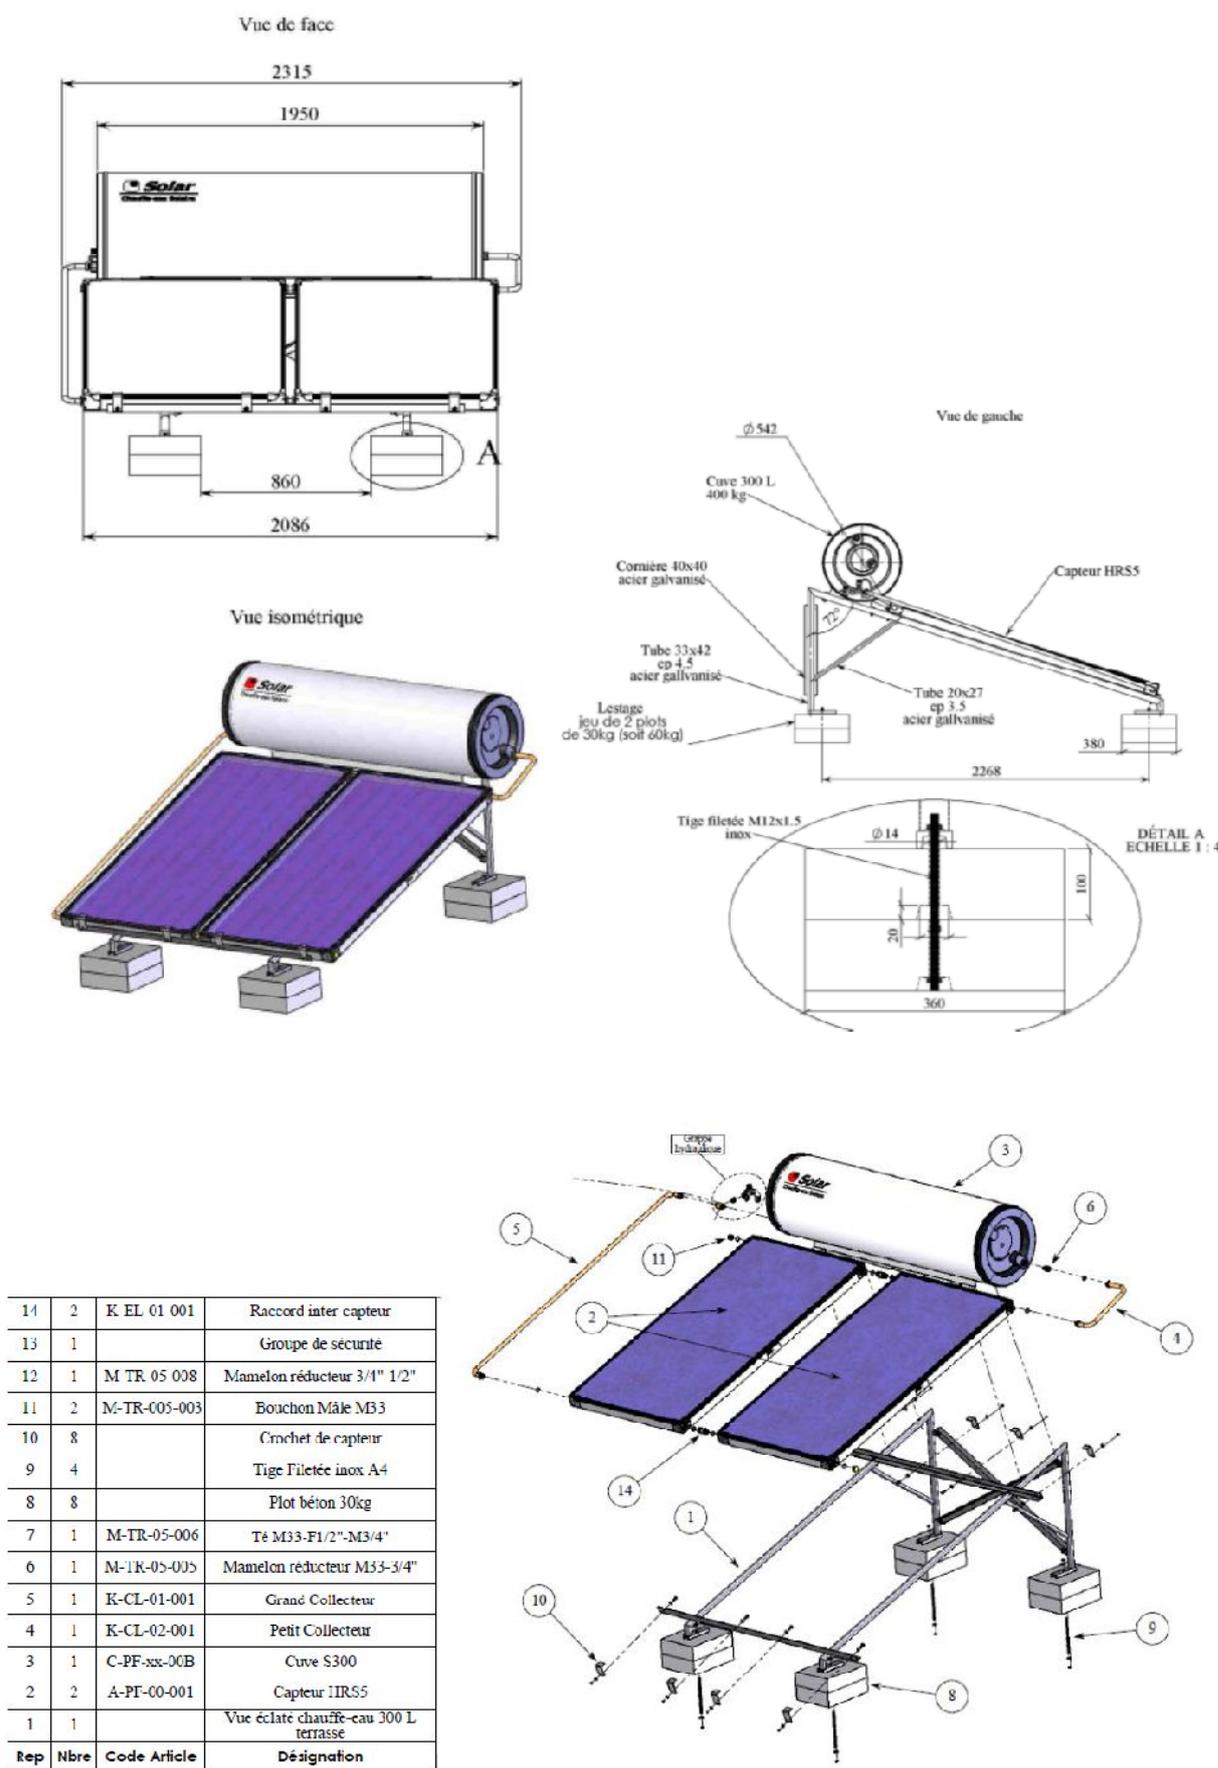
Détail de la mise en œuvre avec dalles de lestage
